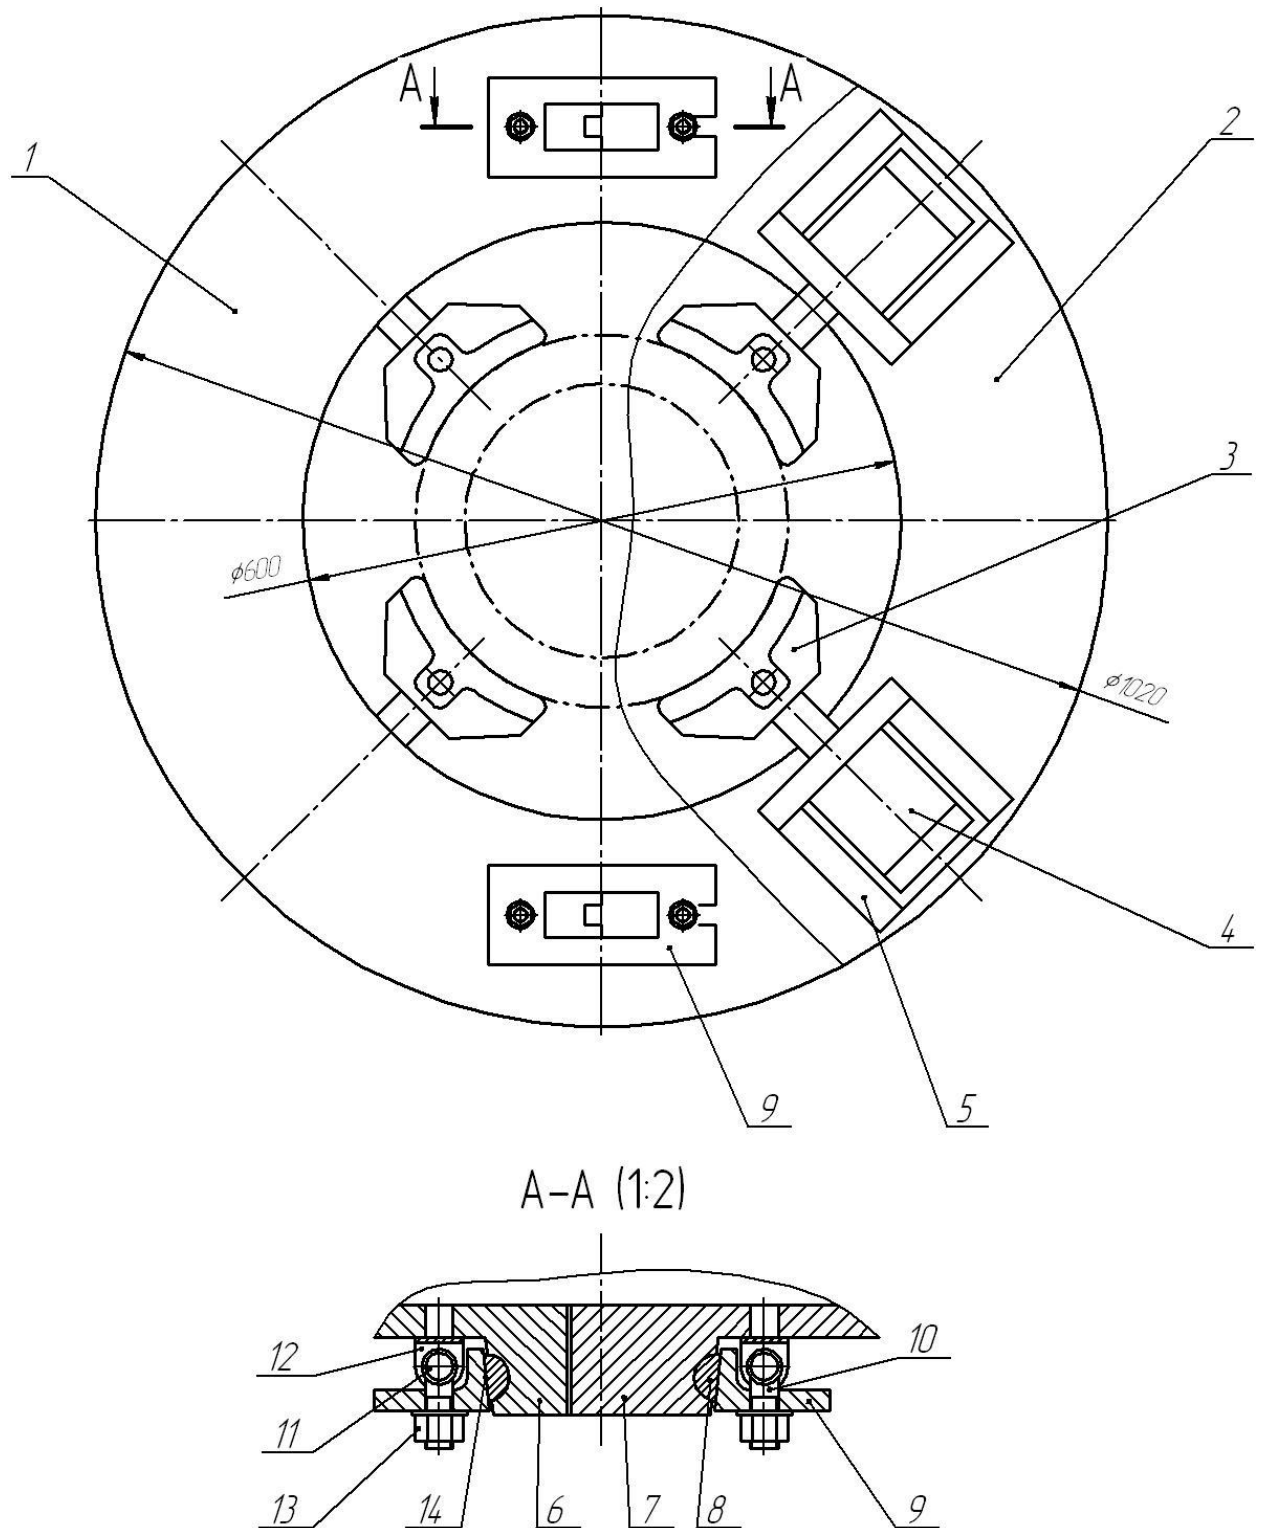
Схема предлагаемого приспособления для сборки стыка труб
